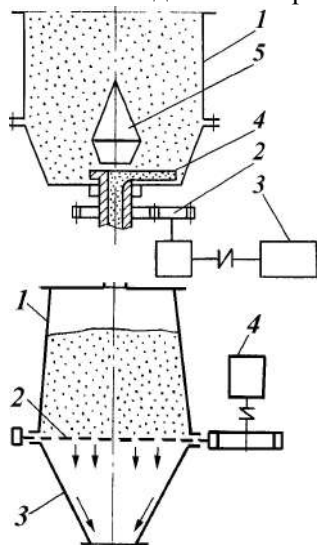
Скребок питатель: 1 – бункер; 2 – зубчатое колесо; 3 – привод;
